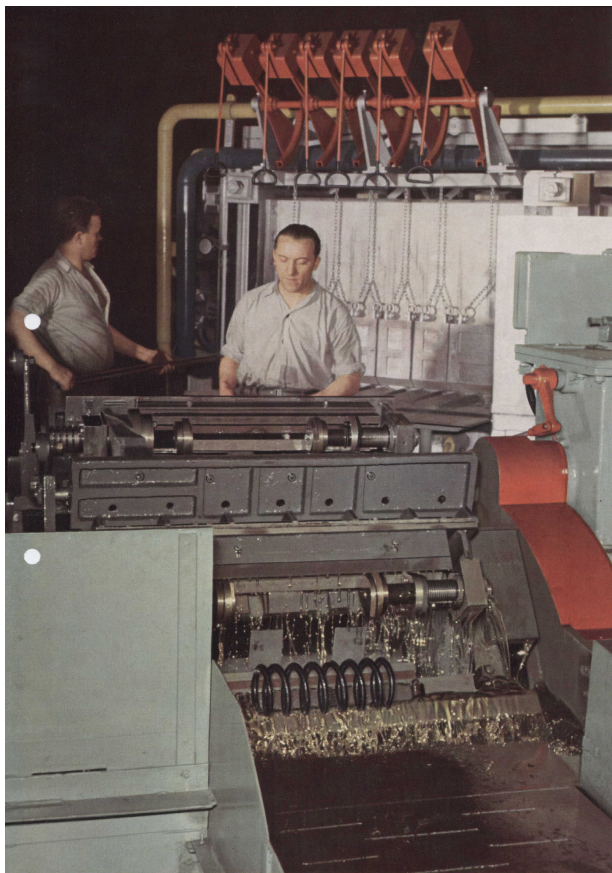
Wickeln von schweren Schraubendruckfedern
